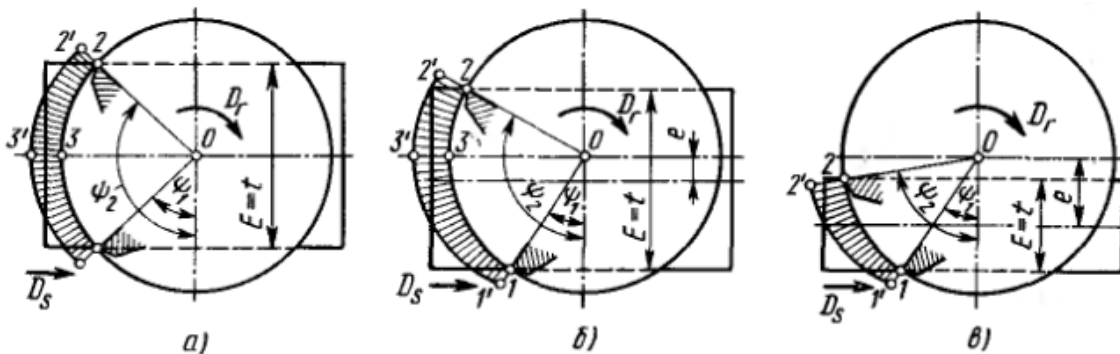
Установка торцевой фрезы относительно заготовки:
